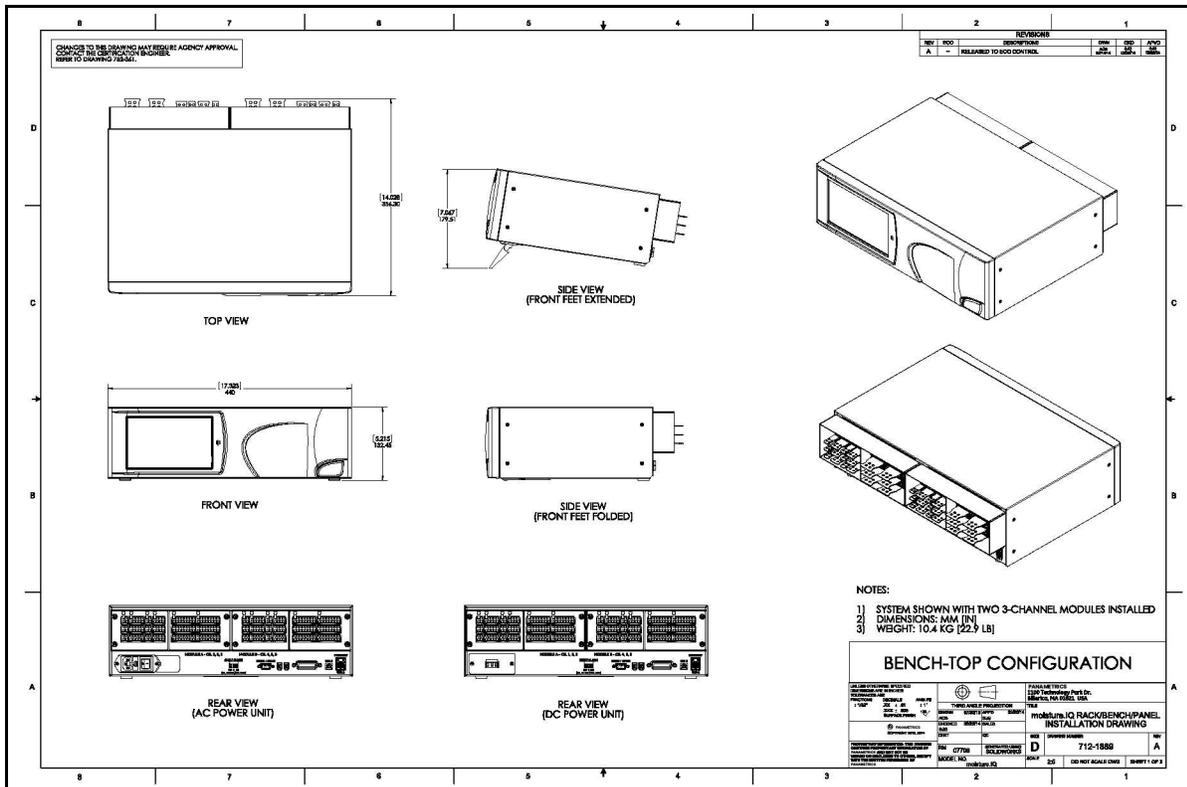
Tischgerät (Zeichnung 712-1889_revA, Blatt 1 von 3)
